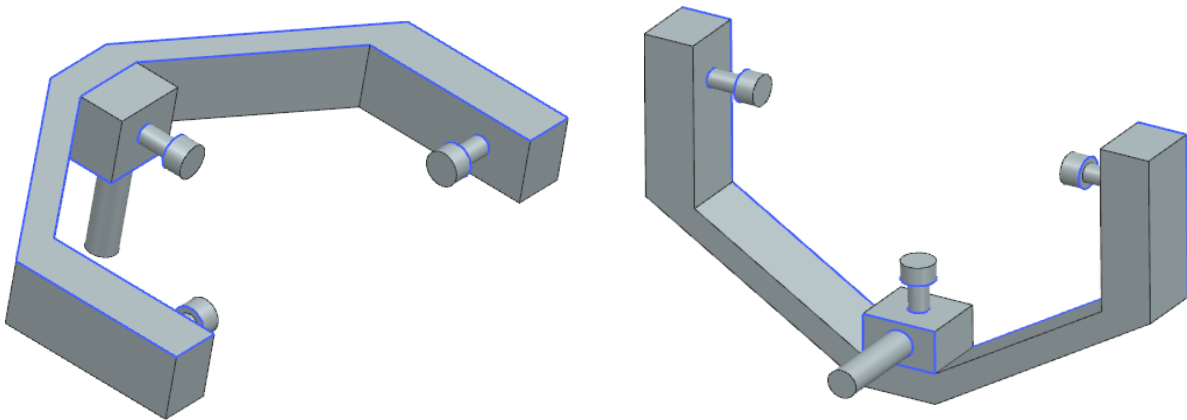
y 56. Diseño en CAD del diseño de la extensión.
